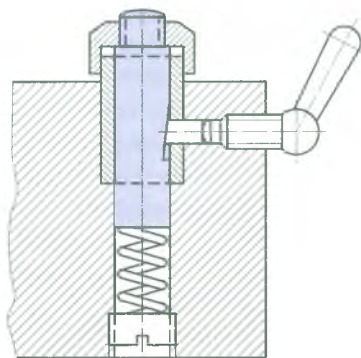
Конструкция самоустанавливающейся подводимой опоры
